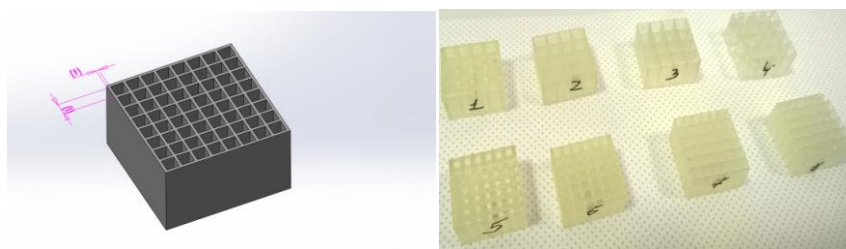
CAD-модель и внешний вид исследуемых образцов
